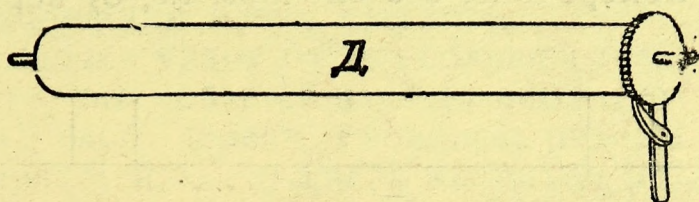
Передний (товарный) навой *Д* с железной шестерней и рычагом.
